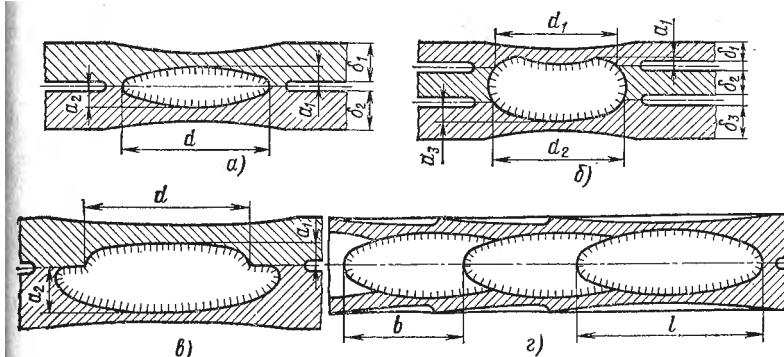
Схемы определения на макрошлифе размеров литой зоны и перекрытия шва
